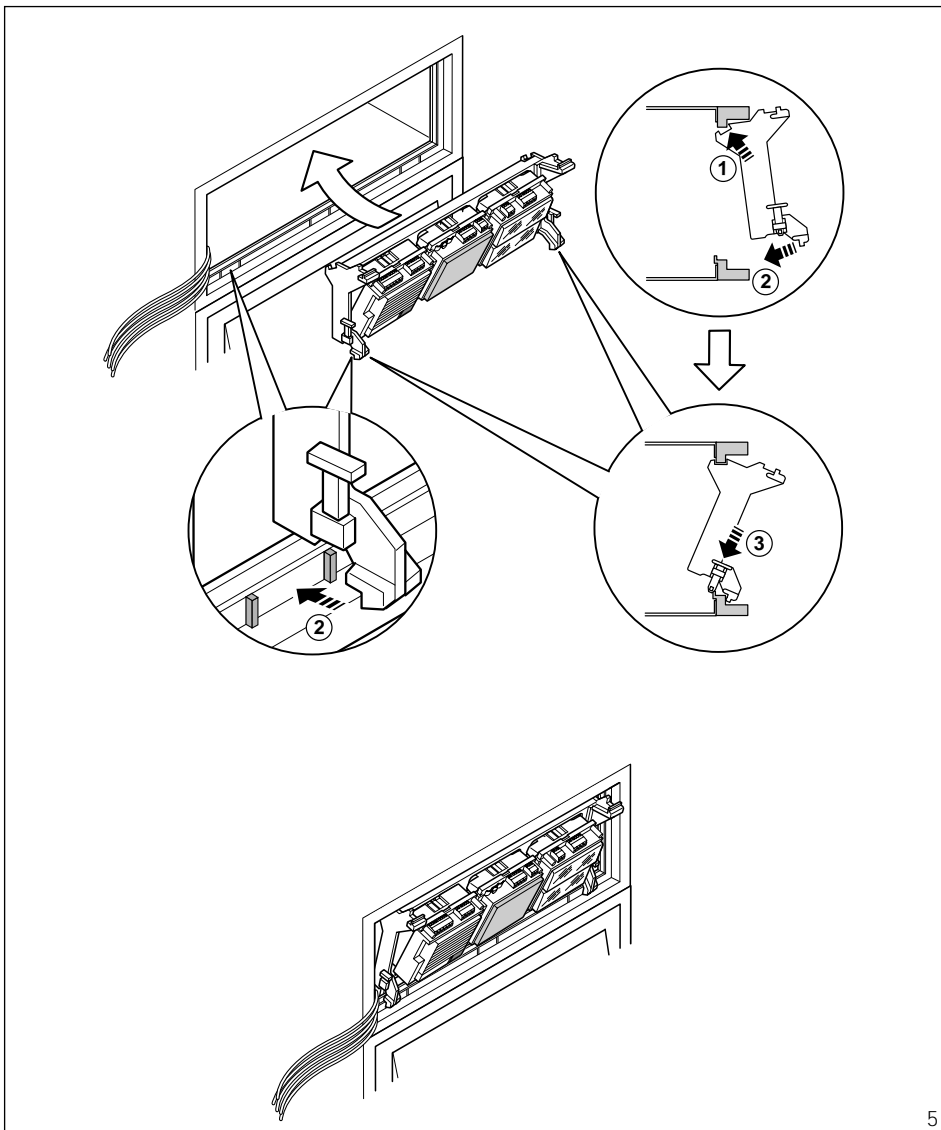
Montage des Chassis mit den Modulen an der Position zur Ausführung der Anschlüsse.
